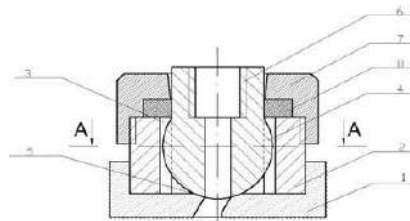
Долото с шарнирным соединением для отклонителей фрезерующего типа. 1-матрица; 2-цилиндрический корпус; 3-шлицевое соединение; 4-шарнир; 5-сферическая проточка; 6-резьба для соединения с ОНД; 7-гайка.
